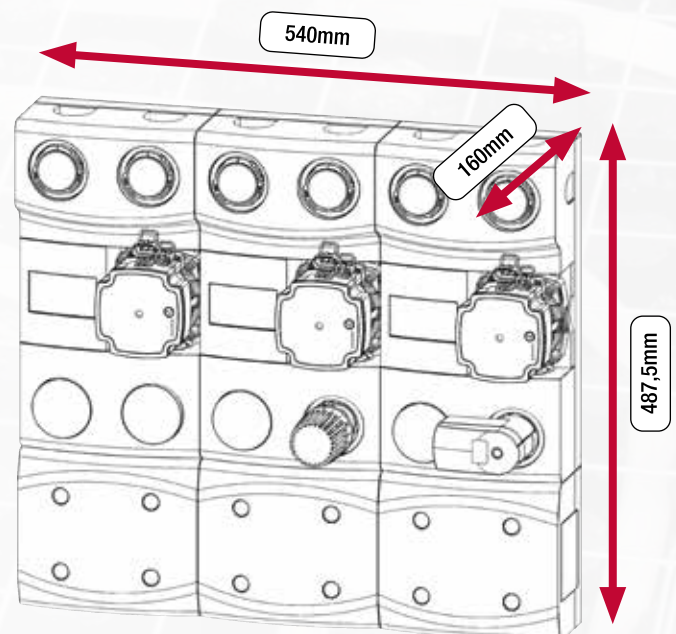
Gesamtabmessungen der kompletten Baugruppe
